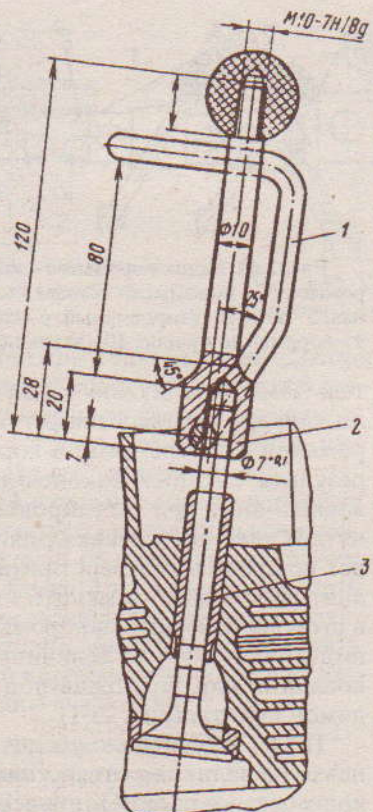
Приспособление для притирки клапанов: 1 - зажим; 2 - оправка; 3 - клапан
